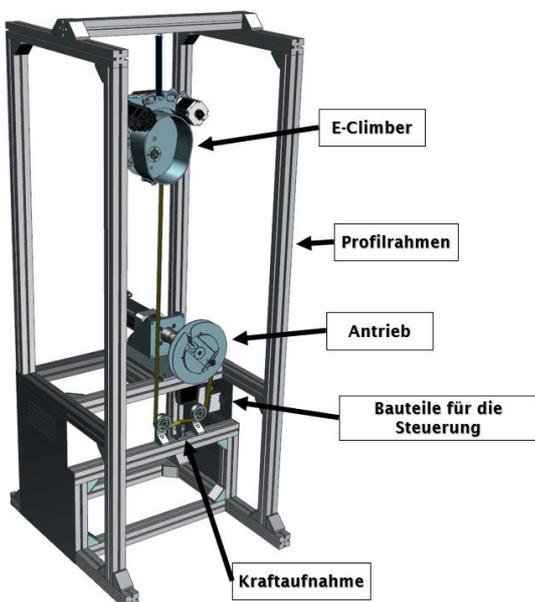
Aufbau der gesamten Baugruppe des Prüfstandes
